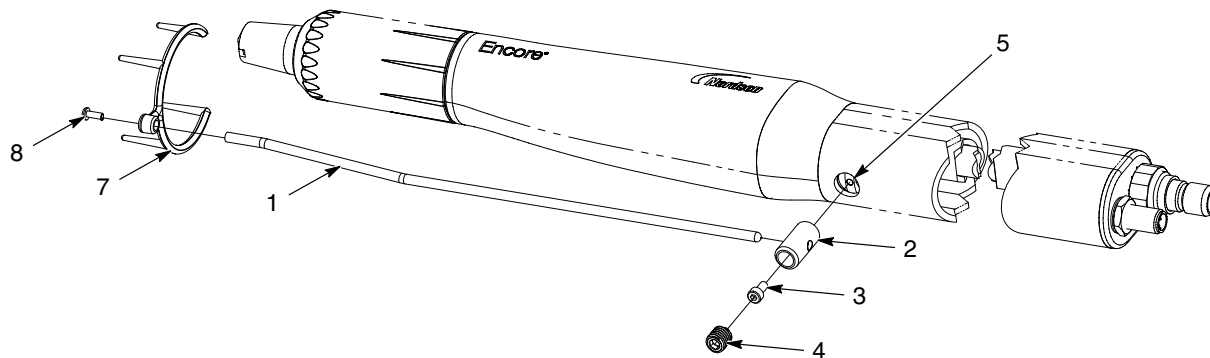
Installazione del collettore di ioni - pistola con montaggio su tubo
